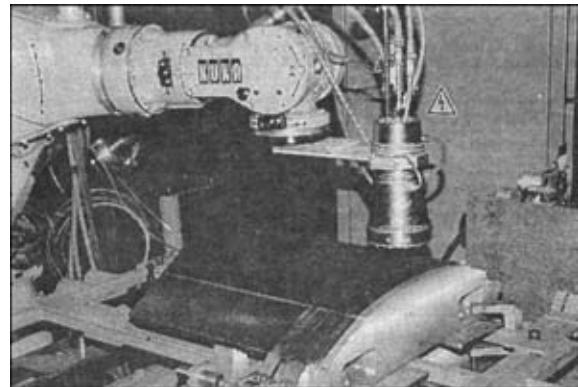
Светолучевое оборудование для сварки и пайки
